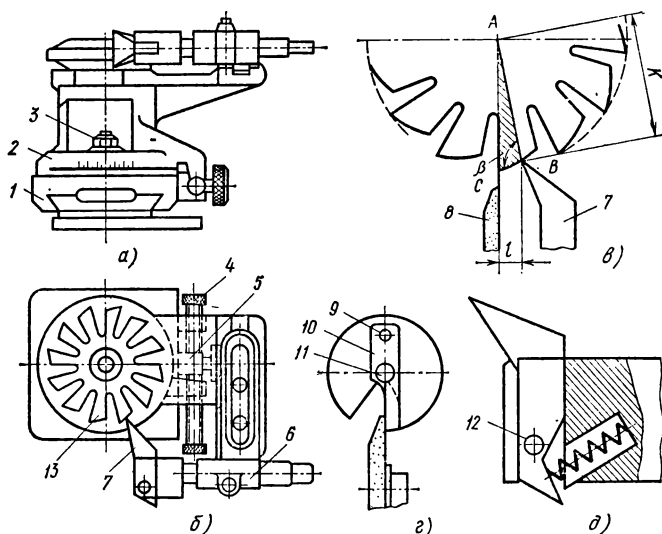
Приспособление для заточки фрез с затылованными зубьями
